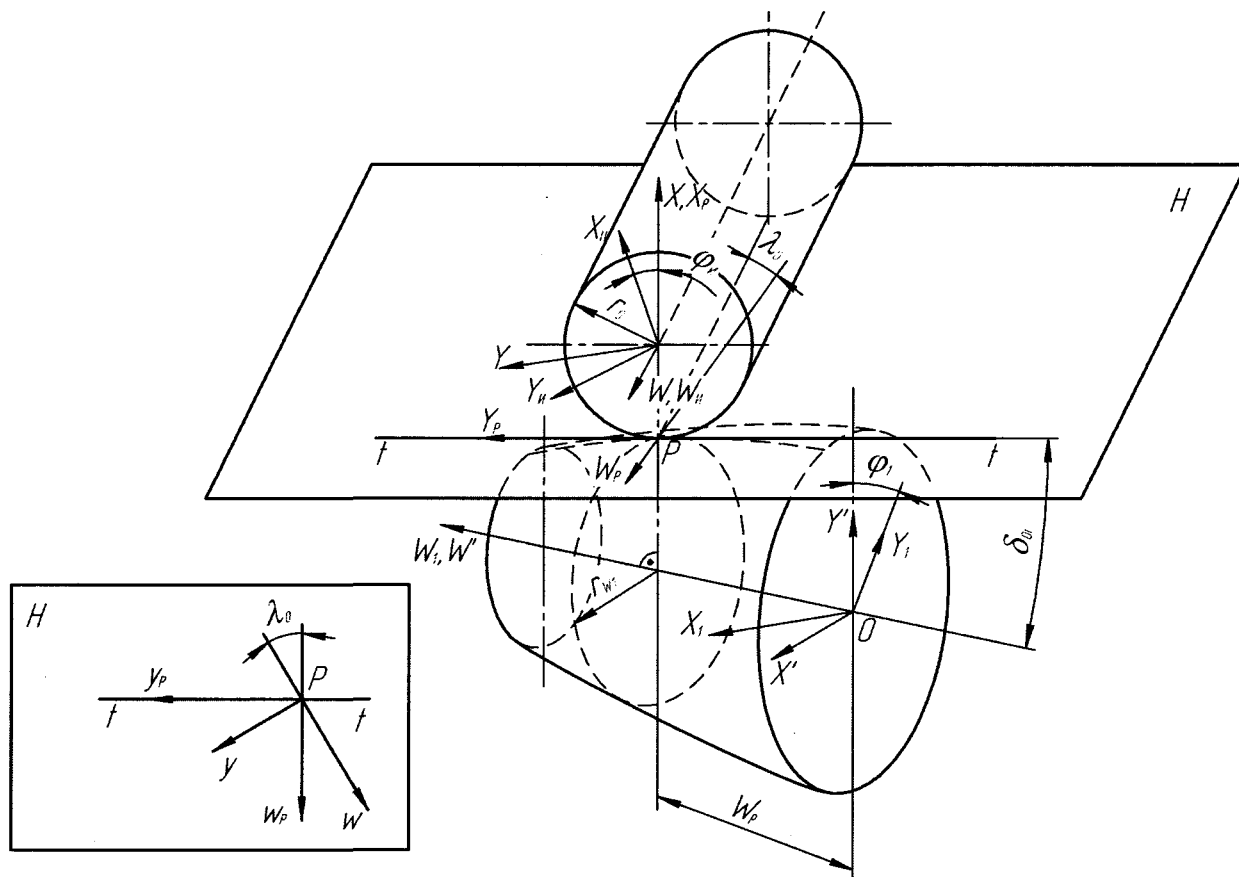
Схема станочного зацепления при нарезании незвольвентной шестерни
